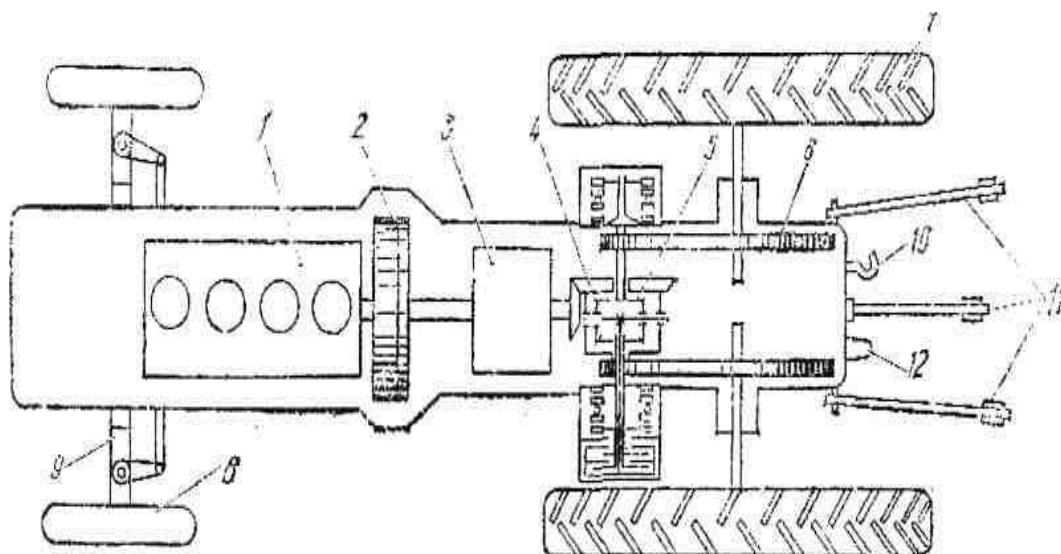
Расположение механизмов и сборочных единиц колесного трактора типа МТЗ-80: 1 – двигатель; 2 – главное сцепление; 3 – коробка передач; 4 – главная передача; 5 – механизм поворота (дифференциал) с блокировочной фрикционной муфтой; 6 – конечная передача; 7 – ведущее колесо; 8 – направляющее колесо; 9 – передний мост; 10 – прицепной крюк; 11 – гидронавесное устройство; 12 – вал отбора мощности.
